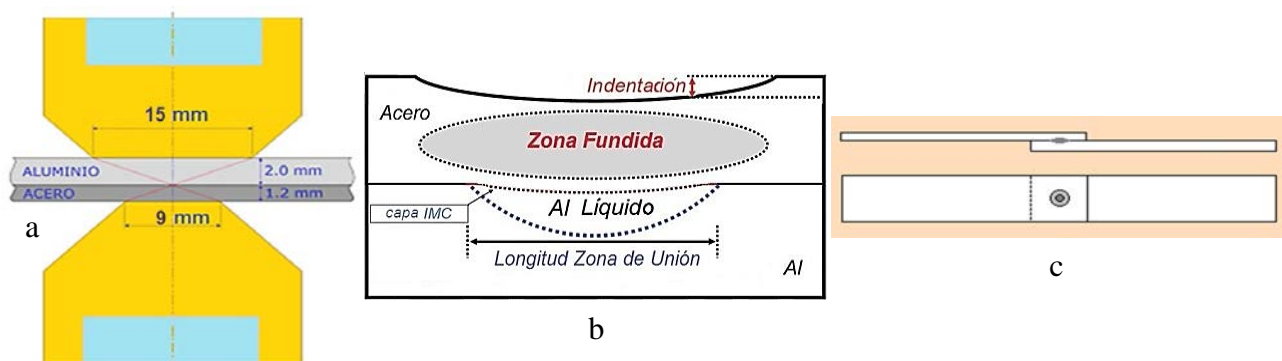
a) Forma y tamaño de la cara activa de los electrodos; b) Esquema de las distintas zonas de un punto soldado de acero-aluminio; c) Esquema de probetas para ensayo de shear-test
